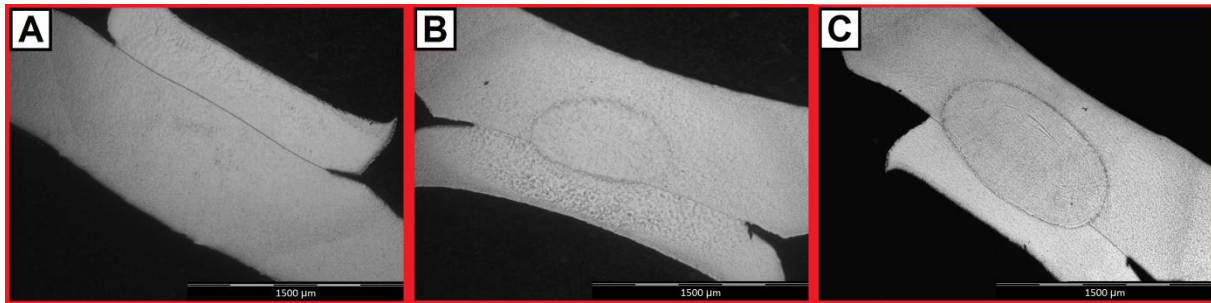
Lentilha de Solda Mínima: A - Ausência de lentilha de solda; B- Lentilha de solda pequena (menor que 1 mm²); C- Lentilha de solda Mínima (aproximadamente 1mm²)
